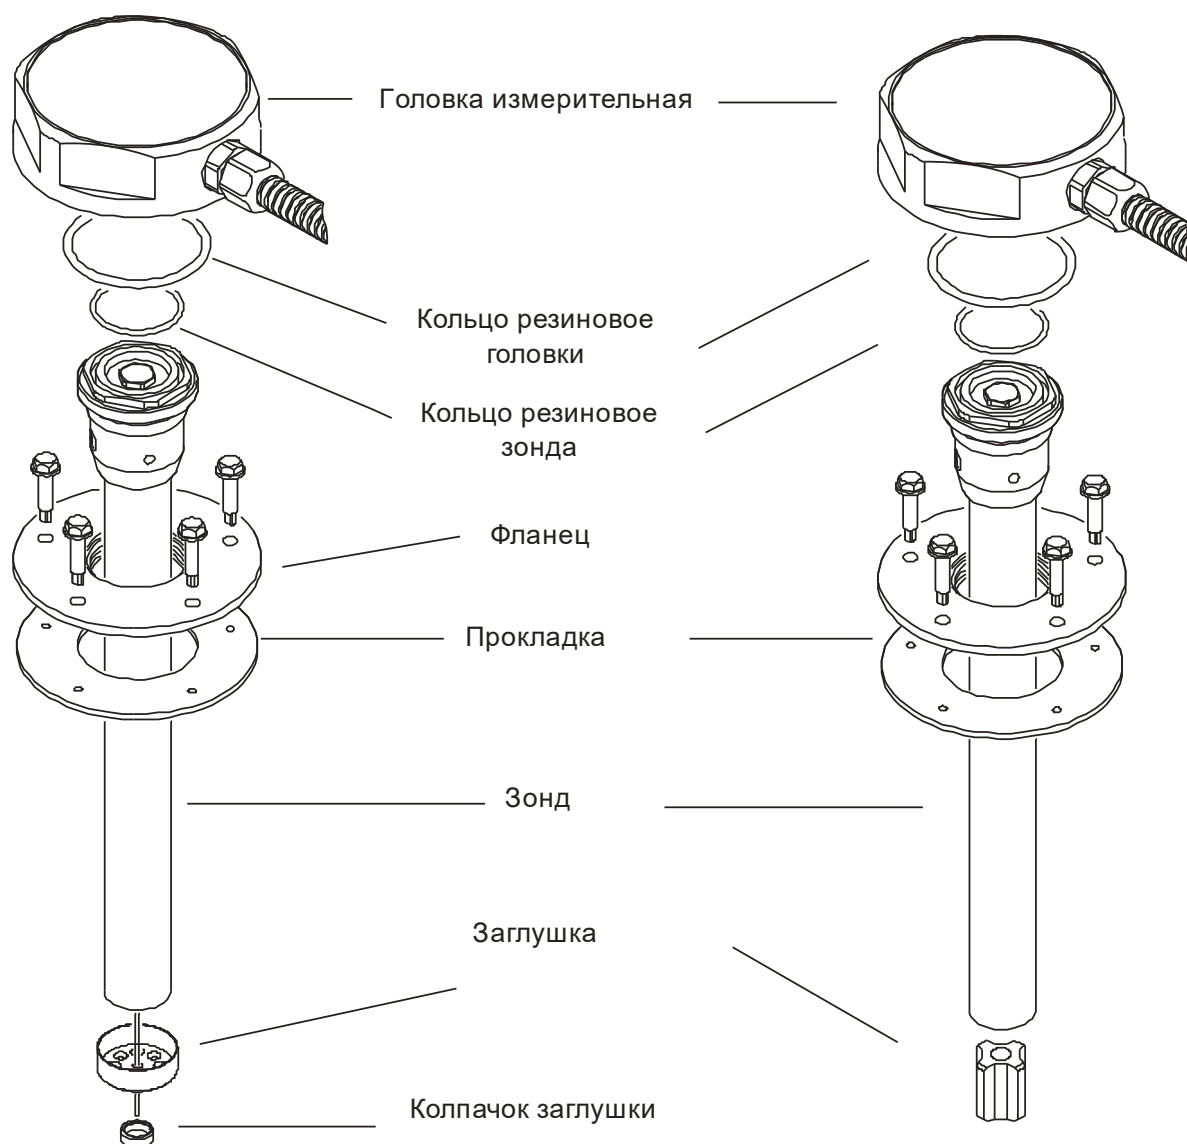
Общий вид датчиков с центральным контактом в виде струны (слева) и в виде штыря (справа)
